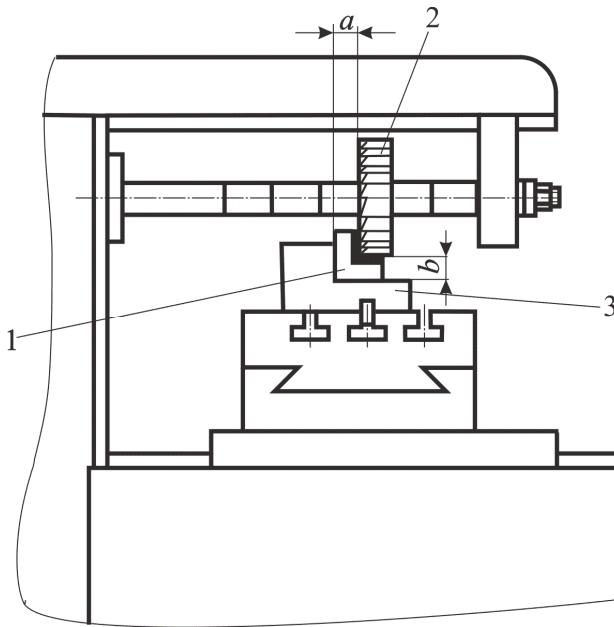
Положение заготовки 1 при обработке уступа на горизонтально-фрезерном станке
